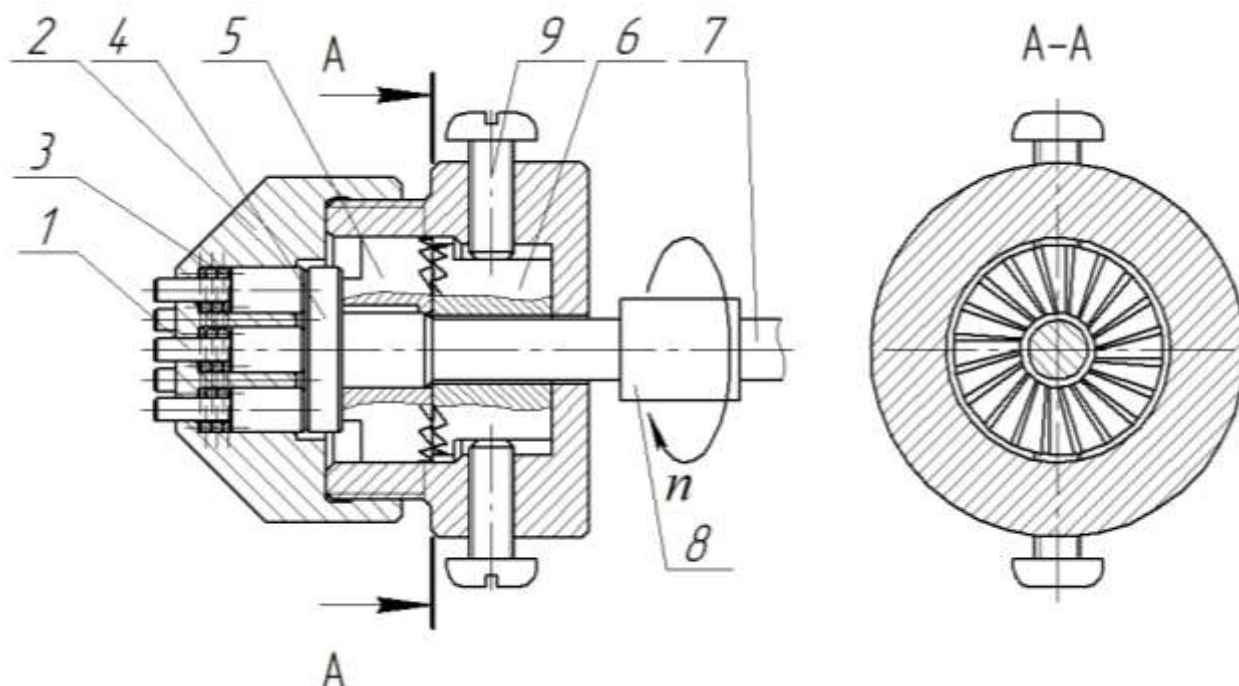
Общий вид устройства для поверхностно-пластического упрочнения:
